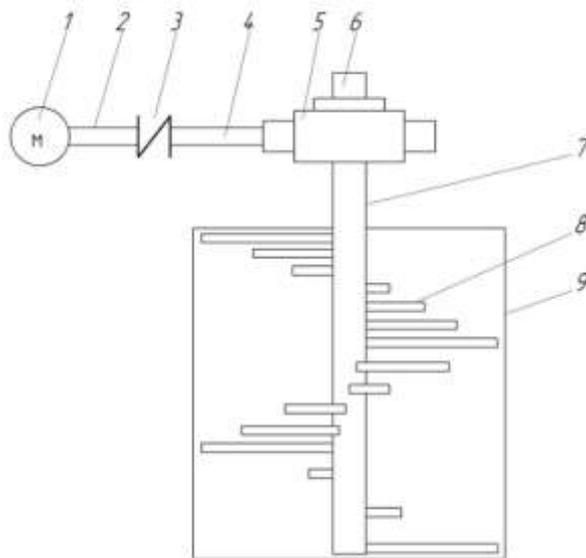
Схема тестомесильной машины: 1 – электродвигатель, 2 – вал, 3 – муфта, 4 – входной вал червячного редуктора, 5 – червячный редуктор, 6 – выходной вал червячного редуктора, 7 – вал месильного органа, 8 – месильные рабочие органы, 9 – дежа
